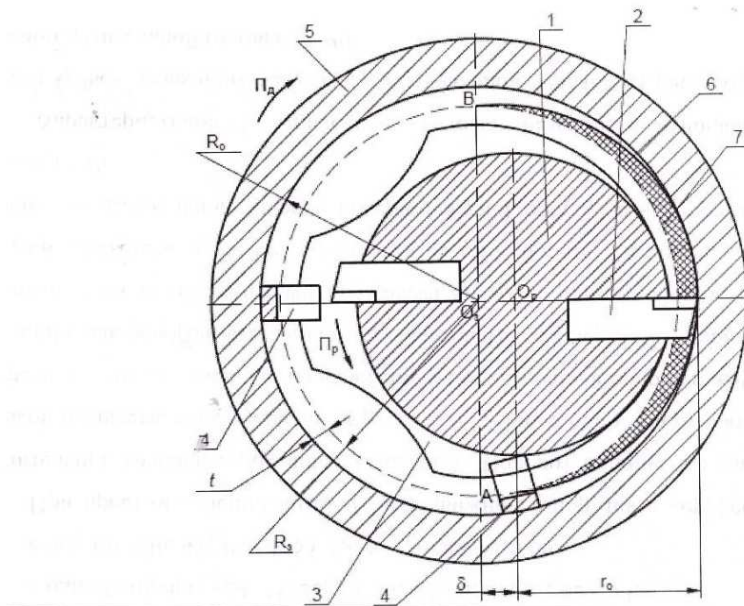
Схема вихревого растачивания отверстий. 1 – резцовая головка; 2- резец-вставка; 3 – борштанга; 4 – направляющая; 5- обрабатываемая деталь; 6 – сегмент срезаемой стружки
